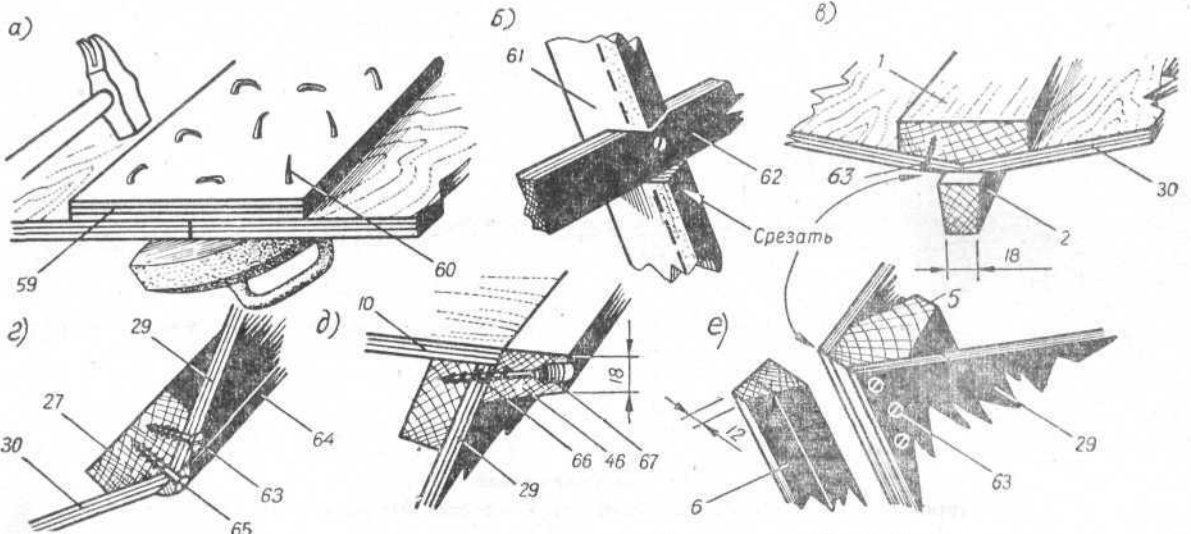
Узлы конструкции корпуса: а — стыковка обшивки на планке; б — малковка набора; в — подгонка фальшкиля; г — защита стыка обшивки на скуле; д — крепление буртика; е — подгонка водореза.
